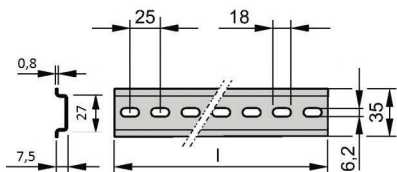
Монтажно-габаритные размеры DIN-рейки DR-n
